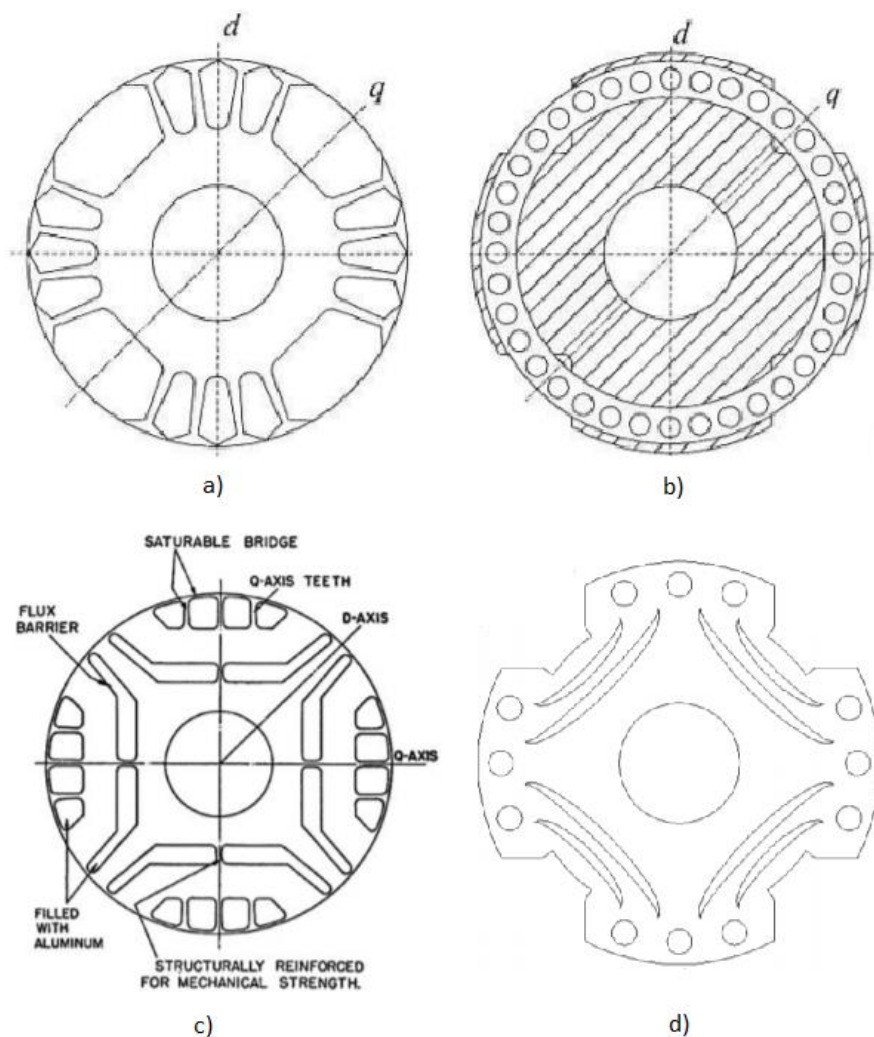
Základní dělení konstrukcí rotorů RSM z hlediska tvaru. a) rotor s vyniklými póly, b) segmentový rotor, c) rotor s bariérami bránícími průchodu magnetického toku, d) axiálně laminovaný rotor, převzato z [13].
